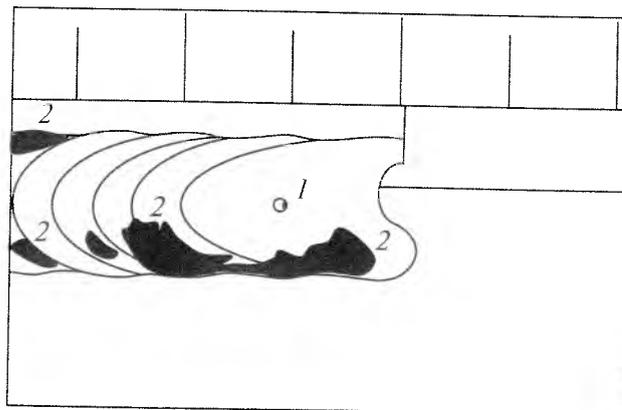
Пора 1 в кратере нахлесточного сварного соединения. Наблюдается также окисление поверхностное в виде пленки оксидов 2 на поверхности шва
